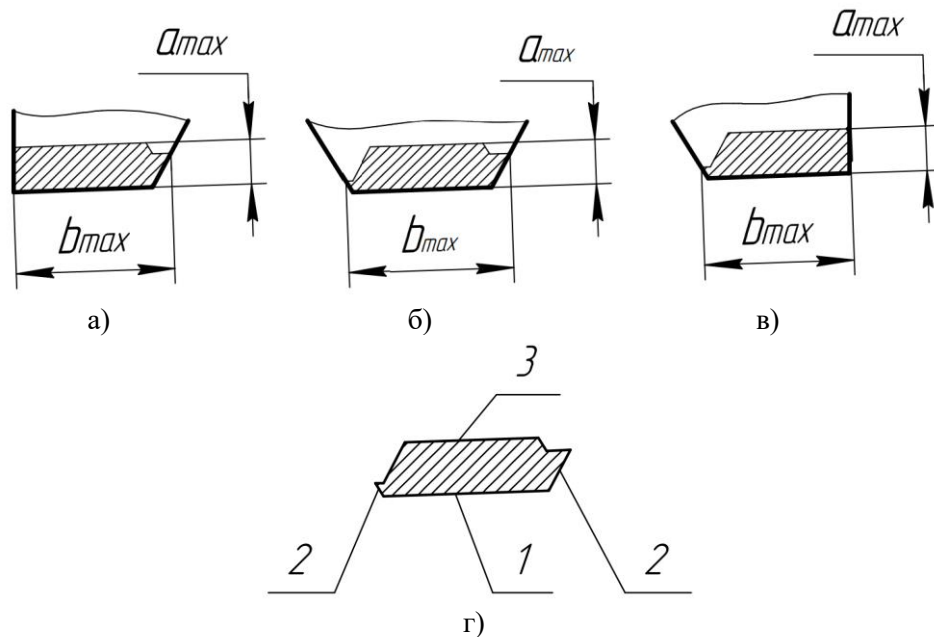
Сечение срезаемого слоя для зуба №1 (а), для зуба №2,3 (б), для зуба №4(в), образование сечения (г): 1 – след главной режущей кромки; 2 – след вспомогательной режущей кромки; 3 – след предыдущих зубьев.
